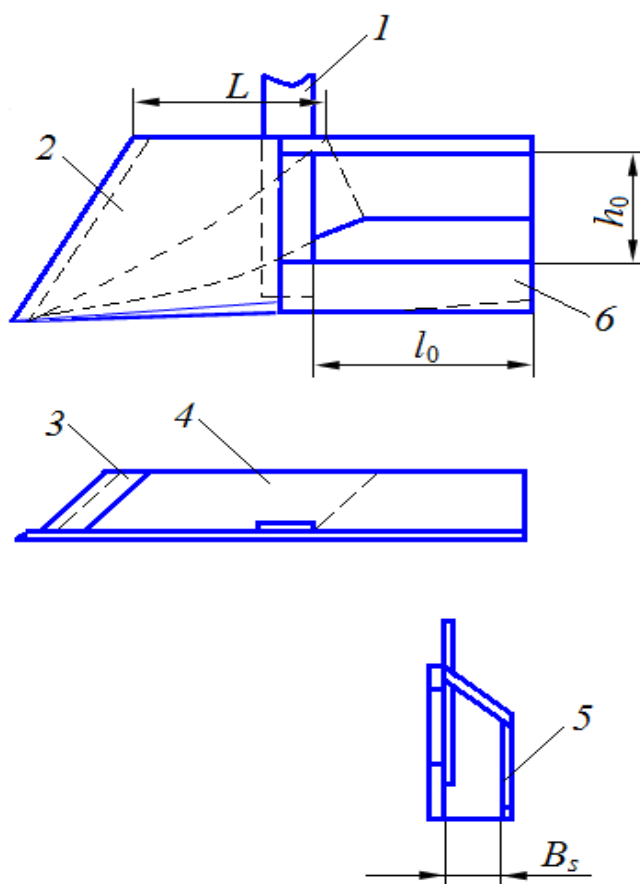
Схема экспериментального щелевателя: 1-стойка 2-большая щека; 3-лемех; 4-почвоподнимающая пластина; 5-маленькая щека; 6-полевая доска.
